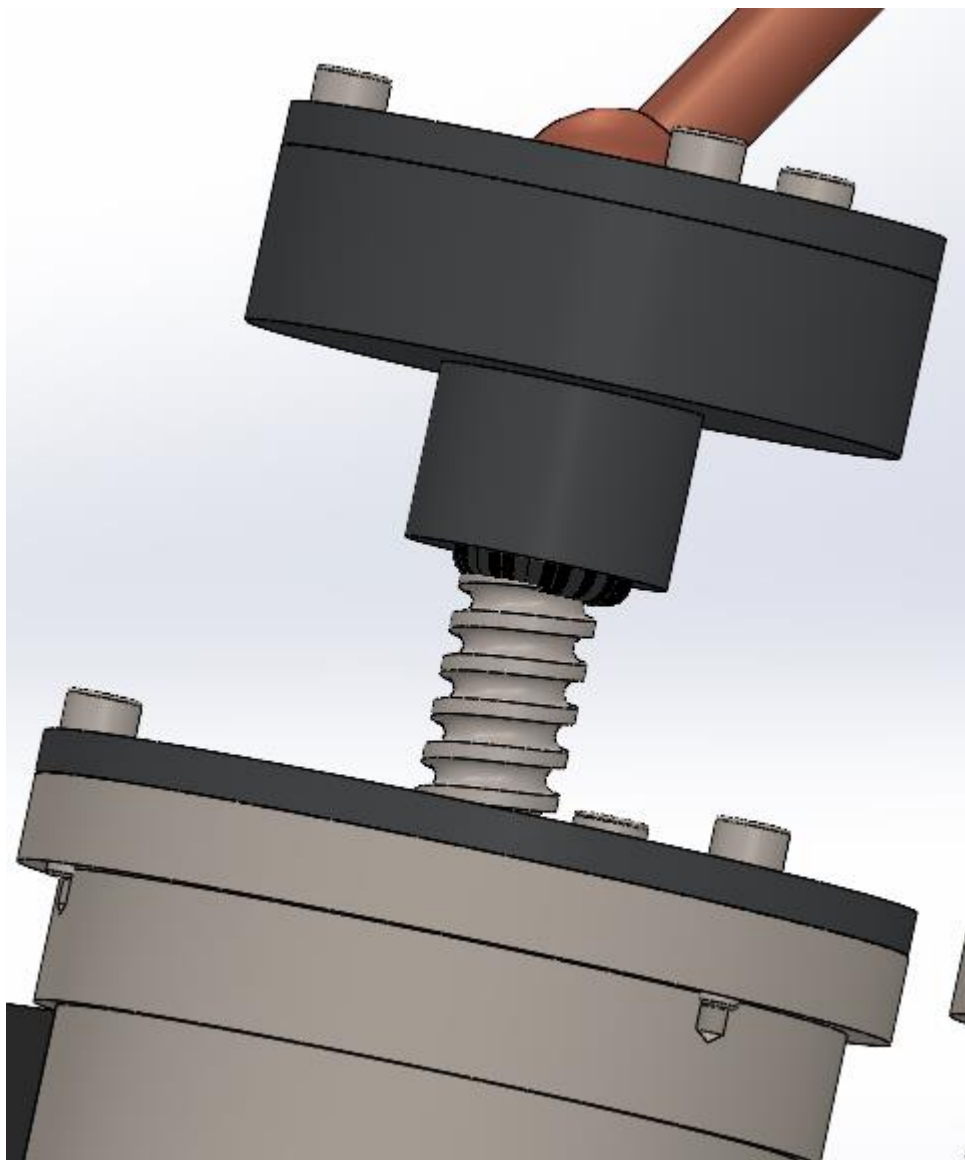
Сварной шов, крепление штанги к толкателю.
